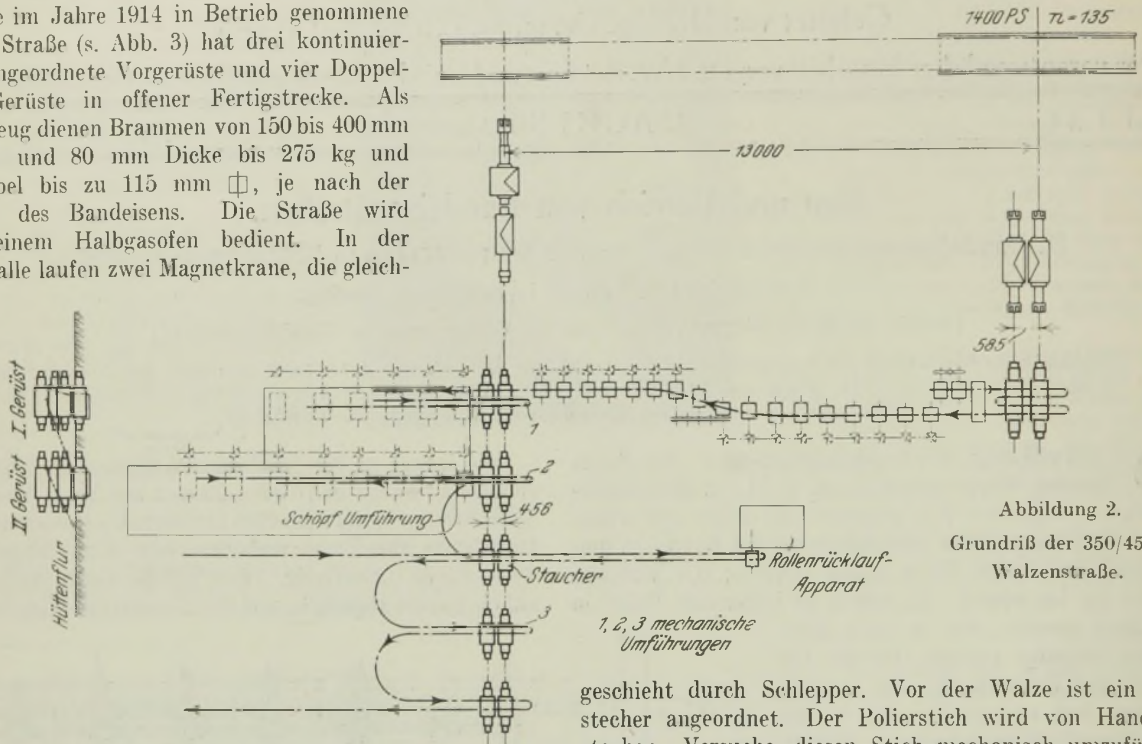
Grundriß der 350/450er Walzenstraße.
